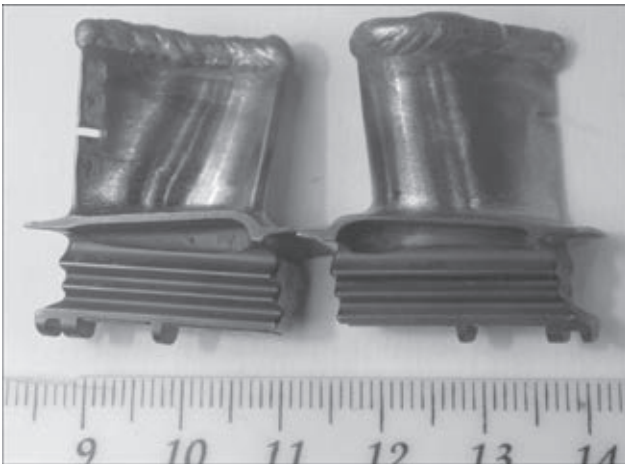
Лопатки после восстановления торца пера (основной и наплавленный металл — сплав ЖС32)
